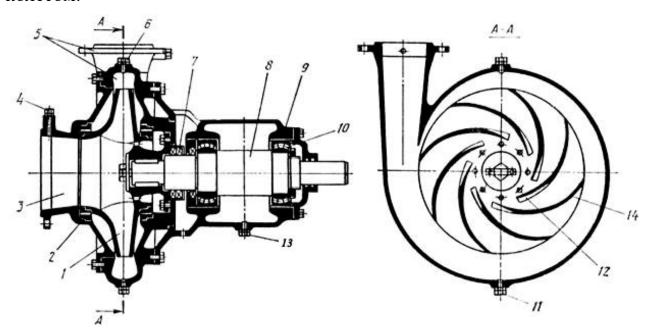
Центробежный одноступенчатый горизонтальный насос типа К I — рабочее колесо; 2 — переднее внутреннее бесконтактное уплотнение; 3 — конфузорный подвод; 4 — пробка отверстия для подключения вакуумметра; 5 — спиральный отвод; 6, 11 — пробка отверстия для подключения вакуумного насоса; 7 — наружное сальниковое уплотнение; 8 — вал; 9 — корпус подшипниковых опор; 10 — подшипник; 11 — масляный щуп; 12 — отверстия для разгрузки рабочего колеса от осевых сил; 13 — пробка сливного отверстия; 14 — лопасть.
